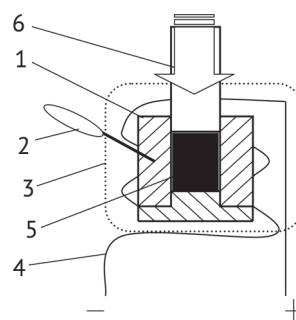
Схема опытной установки с нагревательным элементом для получения брикетов из коксовой шихты: 1 – пресс-форма (матрица), 2 – термометр, 3 – термокожух, 4 – нагревательный элемент, 5 – брикет; 6 – штемпель
